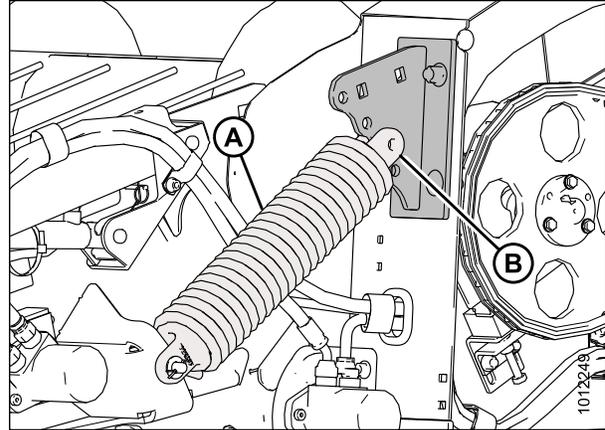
Se muestra el anclaje del lado izquierdo; lado derecho opuesto.
